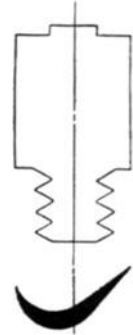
Gleichdruckschaufel der Tosi-Turbine.
